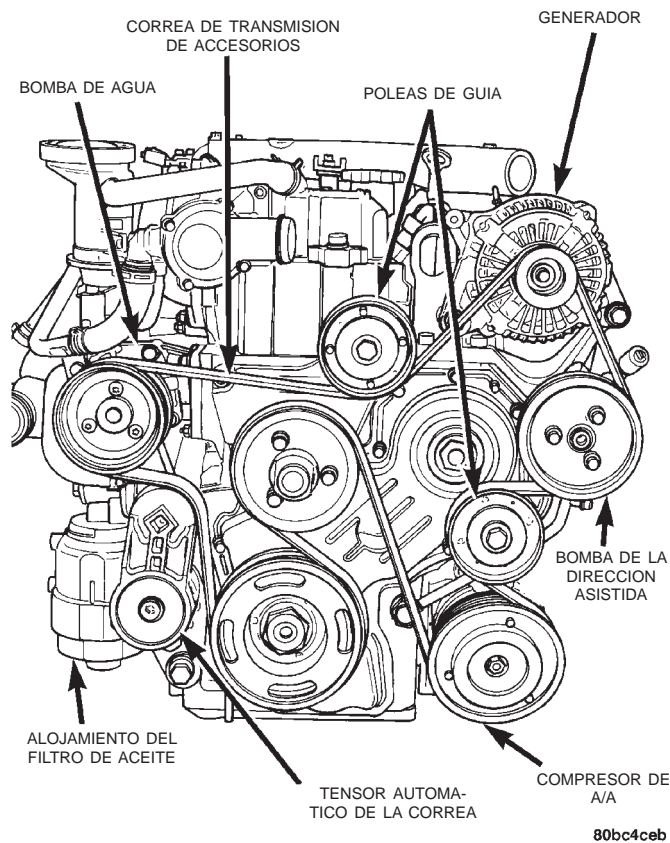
Transmisión de accesorios del motor 3.1L Diesel
